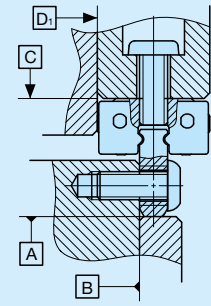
Superfície de montagem de referência de LWL1...Y e estrutura de montagem típica ②
